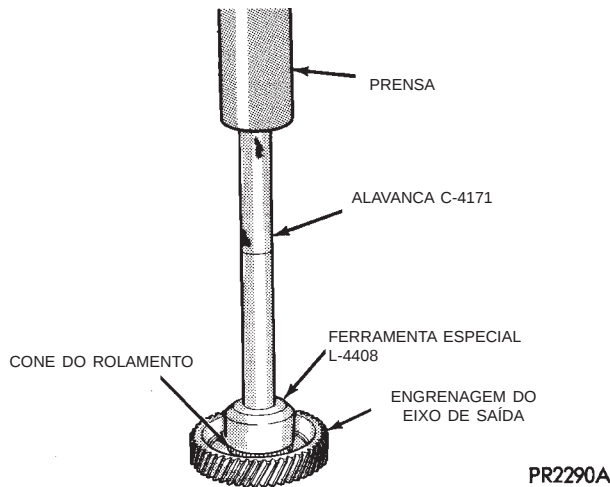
Instalação do Cone de Rolamento da Engrenagem do Eixo de Saída
